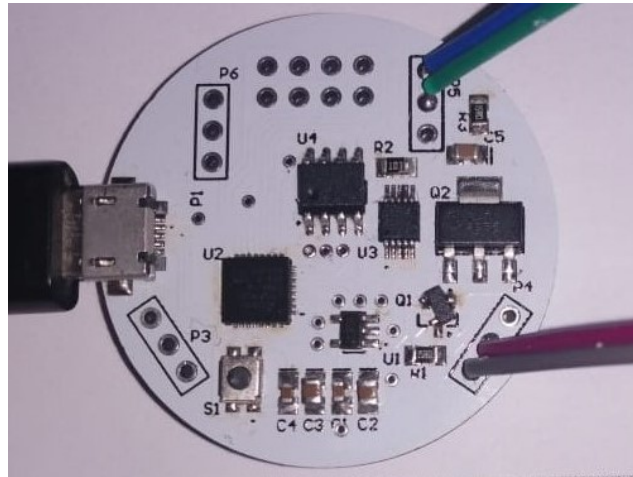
Aspecto físico del PCB fabricado y con componentes soldados.
